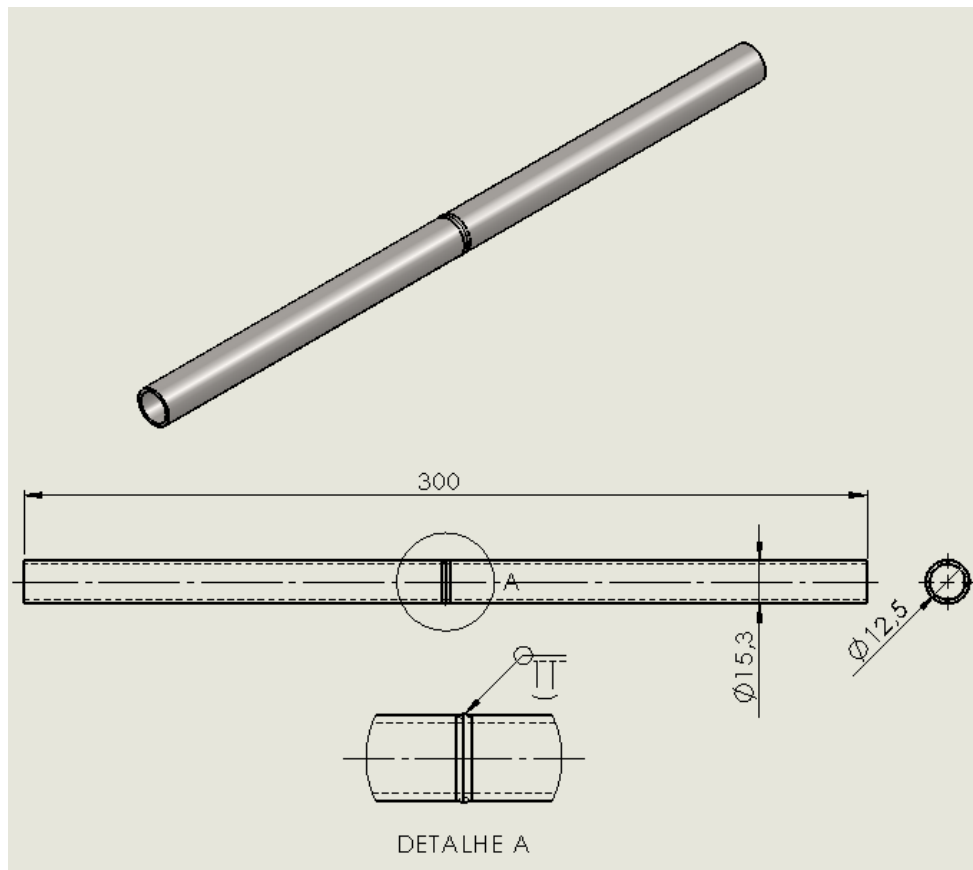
Desenho Detalhado do Tubo Soldado (dimensionamento em milímetros)
